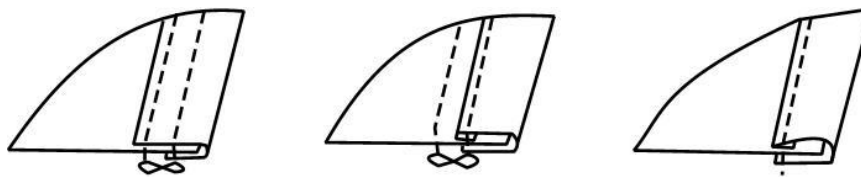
Обробка зрізів деталей обкатувальними швами
